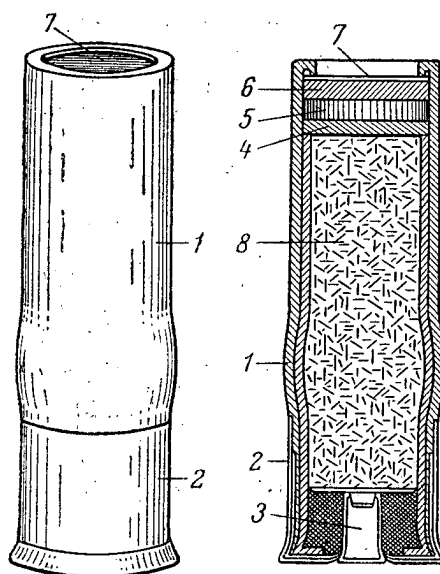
Хвостовой патрон с основным зарядом: 1—бумажная гильза; 2—металлическая шляпка; 3—капсюль; 4—картонный пыж; 5—свинцовый пыж; 6—войлочный пыж; 7—этикетка; 8—порох
